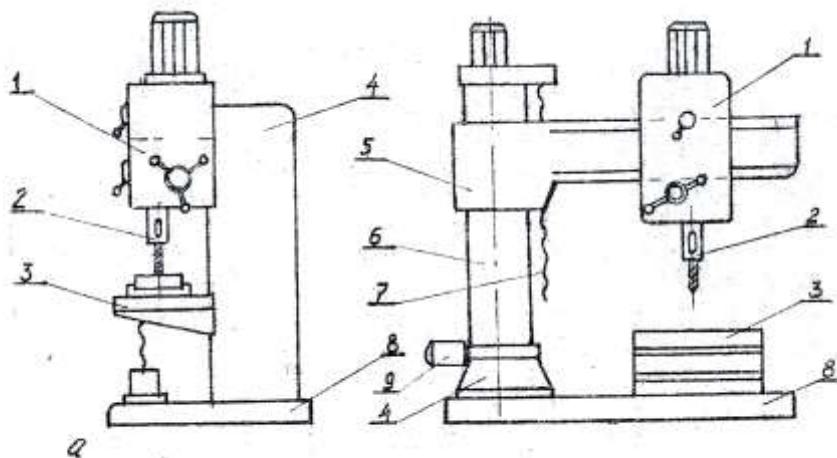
Вертикально-свердлувальний (а) та радіально-свердлувальний верстати (б).
